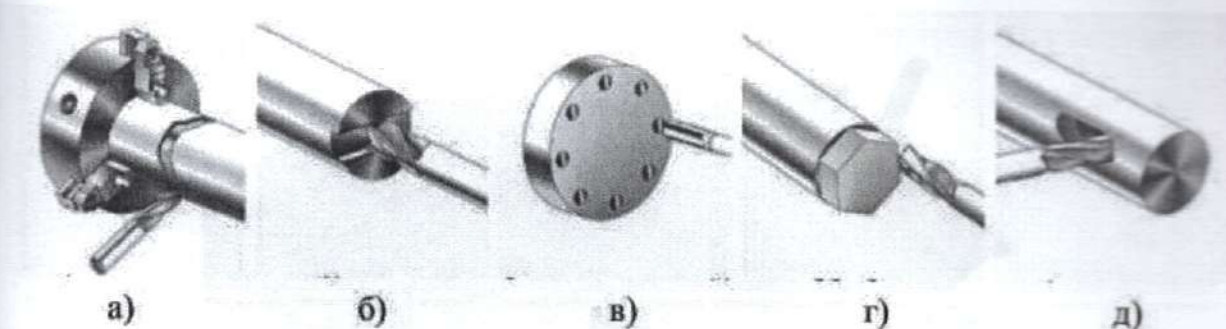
Види обробки на верстатах з револьверною головкою з приводним інструментом: а) Фрезерування криволінійного паза, б) Нарізання торцевого паза, в) Свердління отворів / нарізування різьблення, г) Обробка багатокутників, д) Фрезерування шпоночної канавки.
